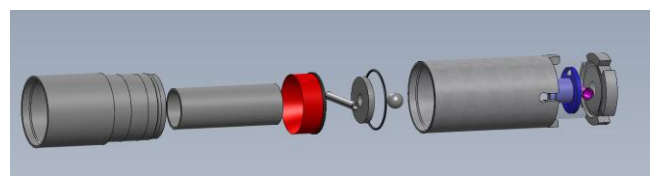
Pied de tubage Hi'Drill® équipé d'un outil perdu et d'un dispositif d'étanchéité.
